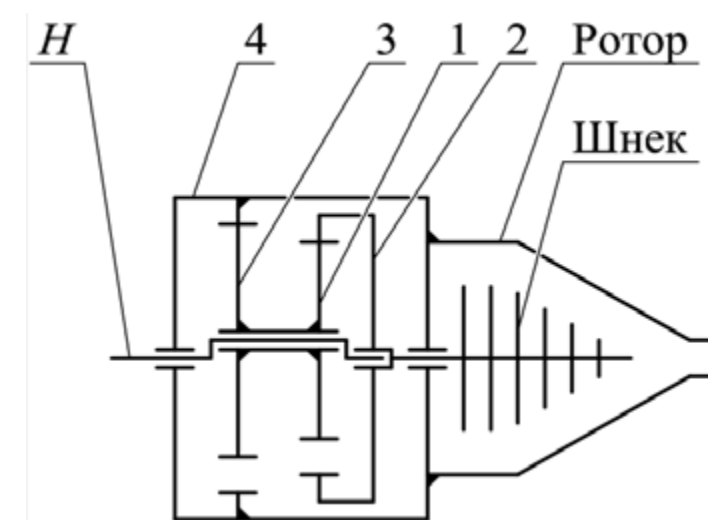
Кинематическая схема редуктора шнековой центрифуги
